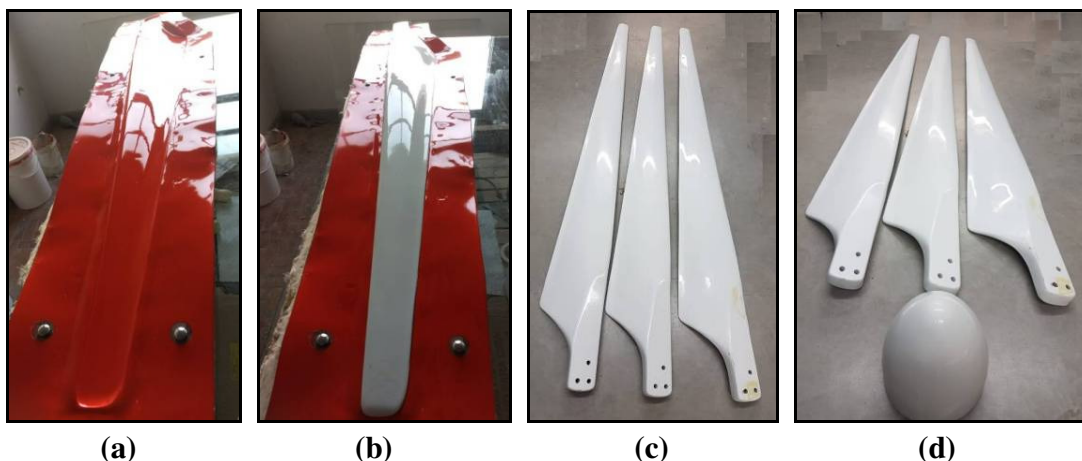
Construção das Pás – (a) Molde – (b) Pá sobre o Molde – (c) Vista das três pás – (d) Vista das três pás com o bico
